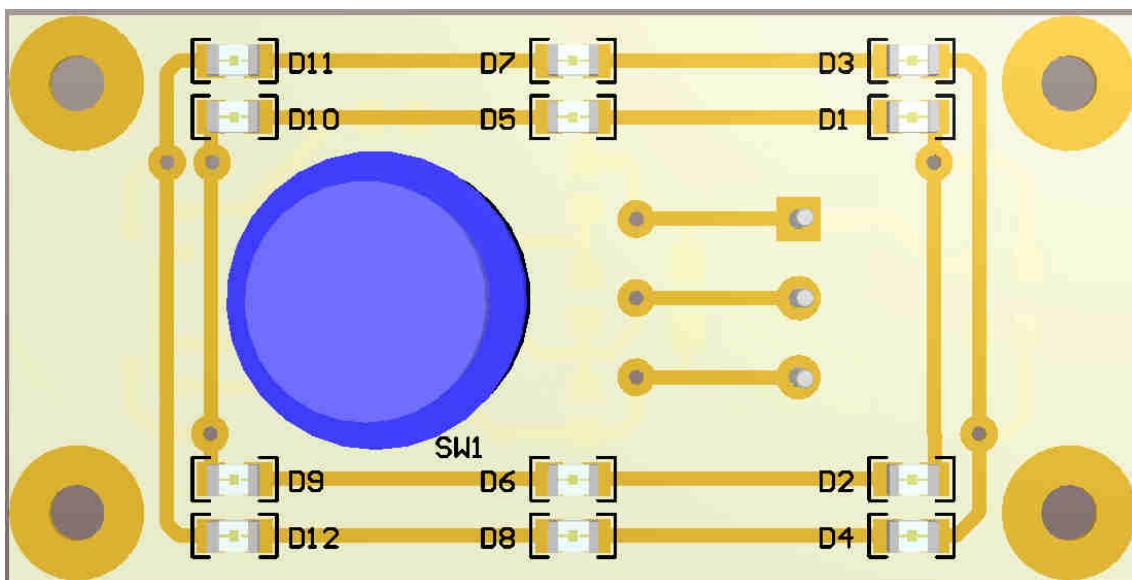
Schemat montażowy płyty głównej modułu dzwonka drzwiowego
